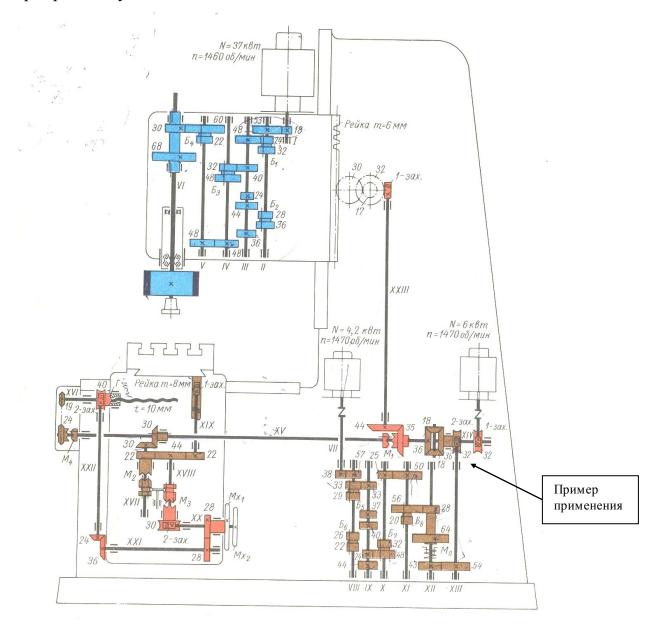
Применение планетарного механизма в вертикальном бесконсольнофрезерном станке мод. 6А54.
